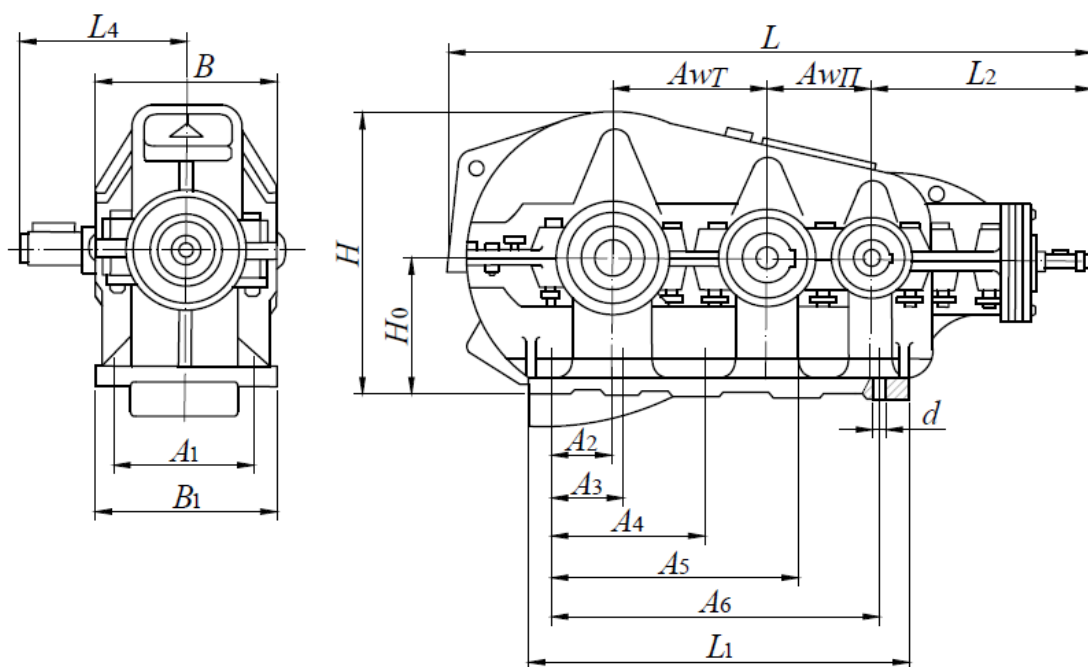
Редуктор трехступенчатый коническо-цилиндрический типа КЦ-2
